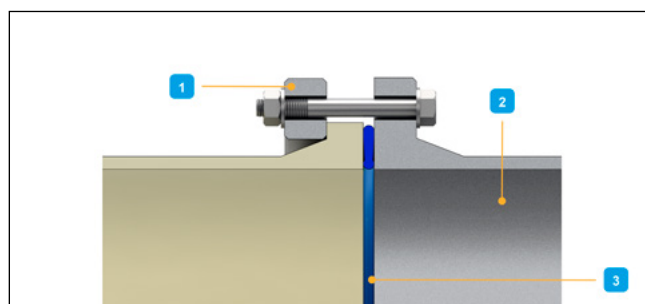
Løsflange i stål eller GRP med profileret ringpakning
